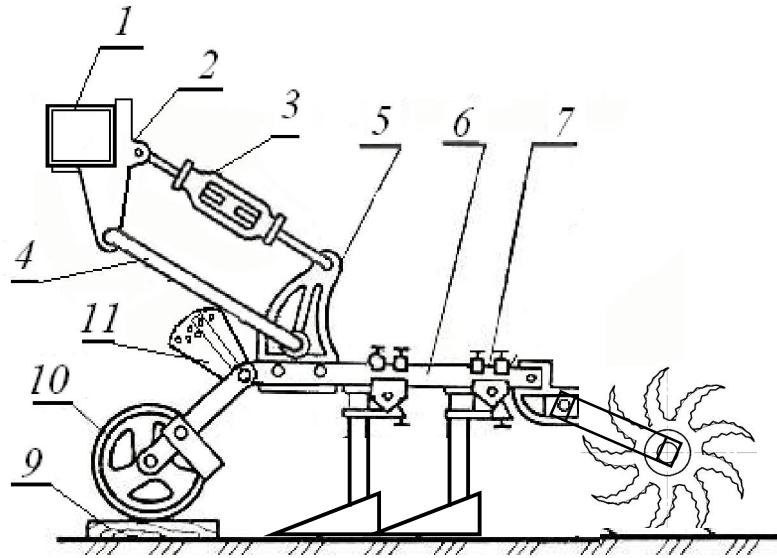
Регулювання глибини обробітку робочою секцією культиваторного агрегату
